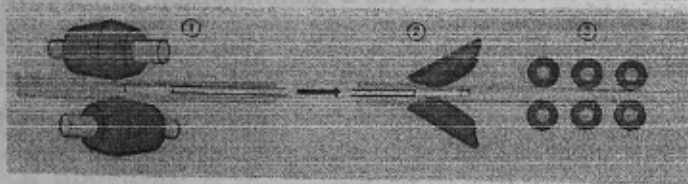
а – Схема установки для изготовления труб с ПКС (1 - прошивной трубопрокатный стан; 2 – ПКС; 3 – редуционный стан)
